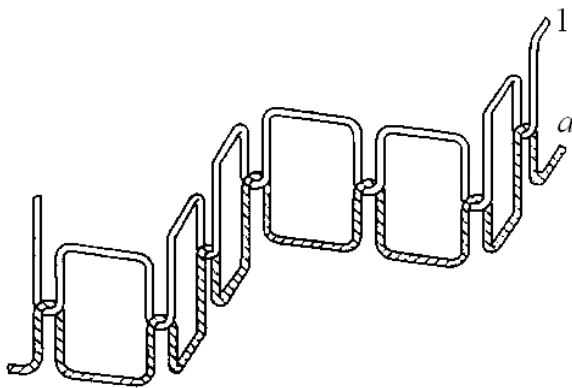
Графічне зображення двониткового човникового зигзагоподібного подвійного стібка типу 308: 1 – нитка голки; *a* – нитка човника
